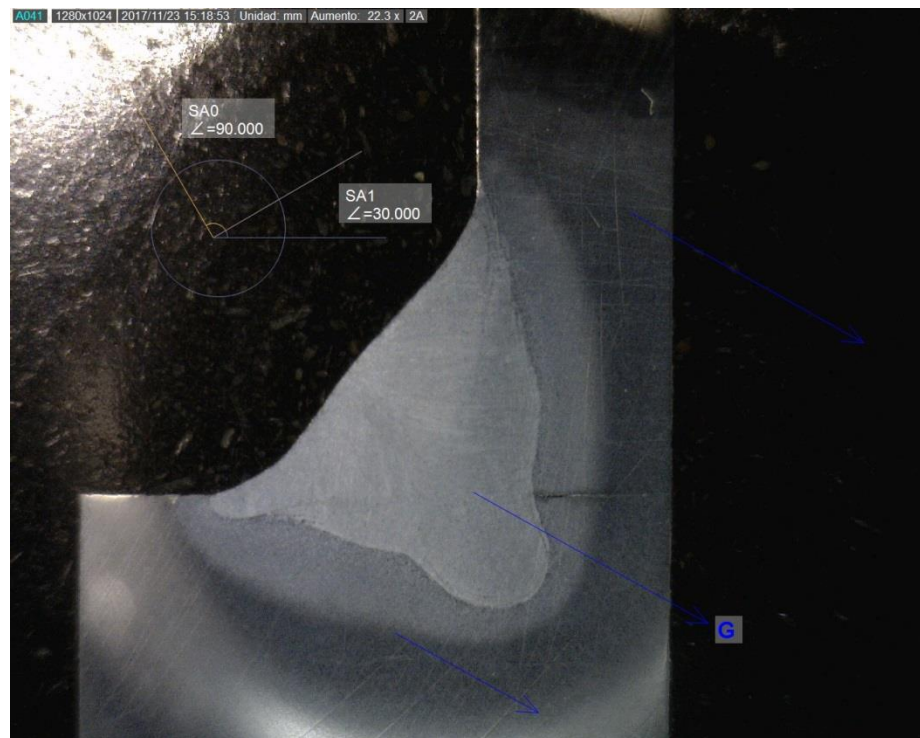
6 Perfil obtenido en cupón de soldadura 3B.
